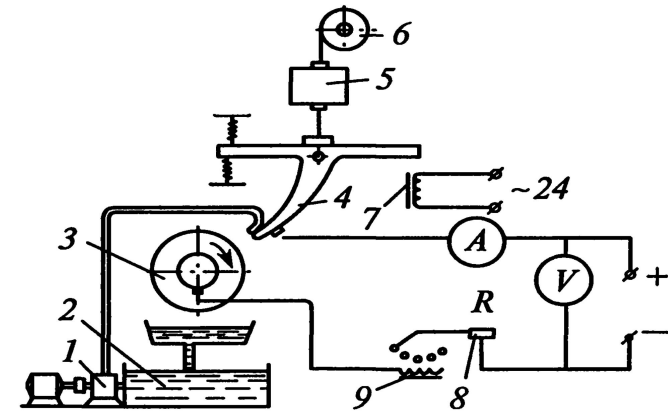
Схема установки для вибродуговой наплавки: 1 – насос; 2 – бак; 3 – деталь; 4 – мундштук; 5 – механизм подачи; 6 – кассета; 7 – вибратор; 8 – реостат; 9 – дроссель
